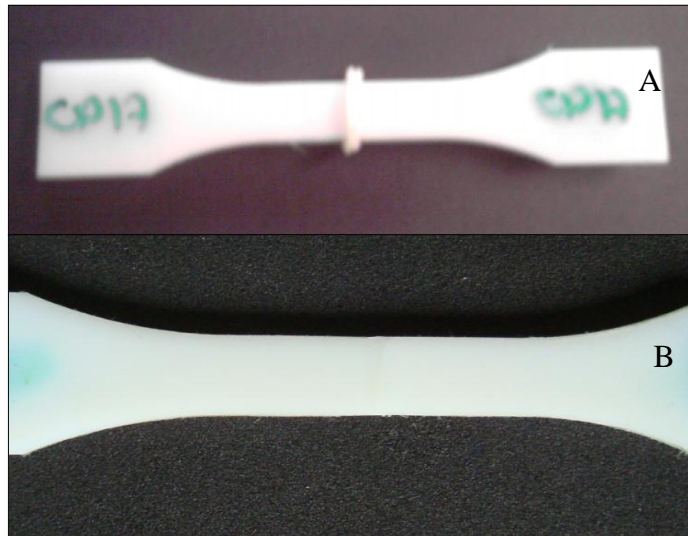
(A) Corpo de solda com cordão de solda (B) Corpo de prova depois de lixado.
